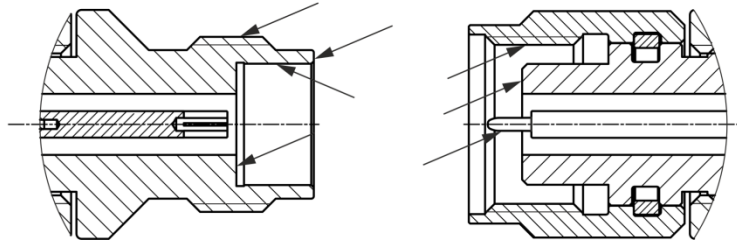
Чистка на примере соединителей 1,85 мм (розетка и вилка)
